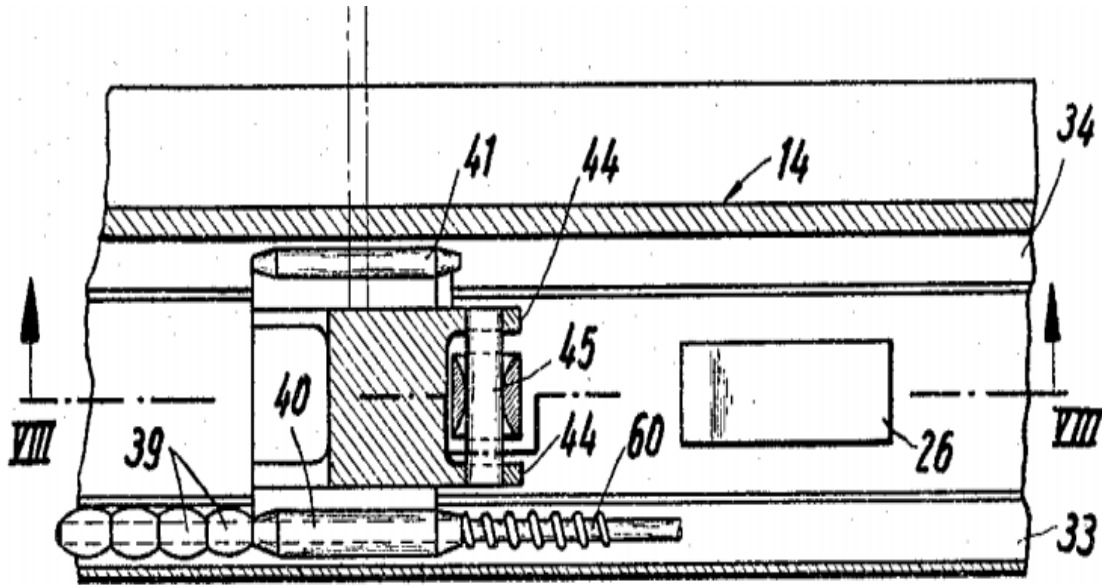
Wilhelm Baier Sunroof Kesiti.
